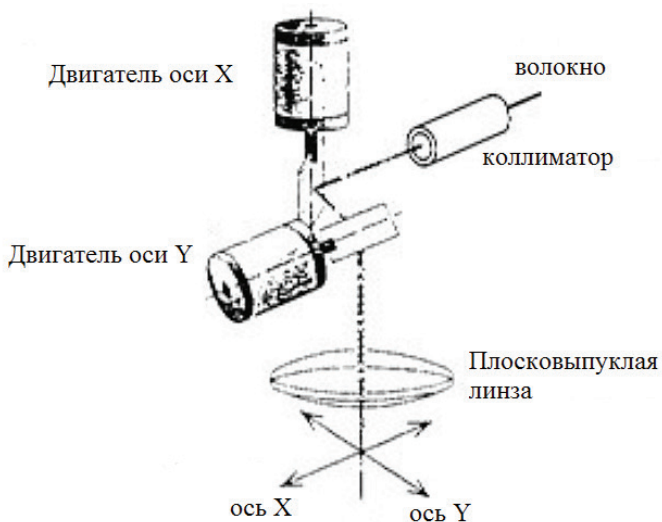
Механизм фокусировки лазерного луча на рабочей поверхности
